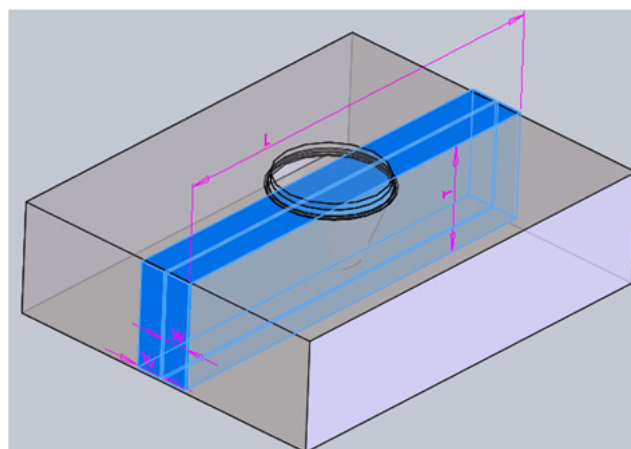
Posição de retirada das amostras para ensaio de dobramento.
